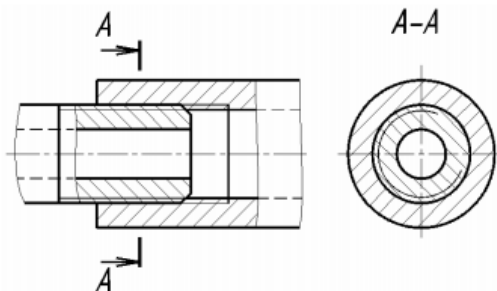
Изображение трубного соединения на цилиндрической резьбе
